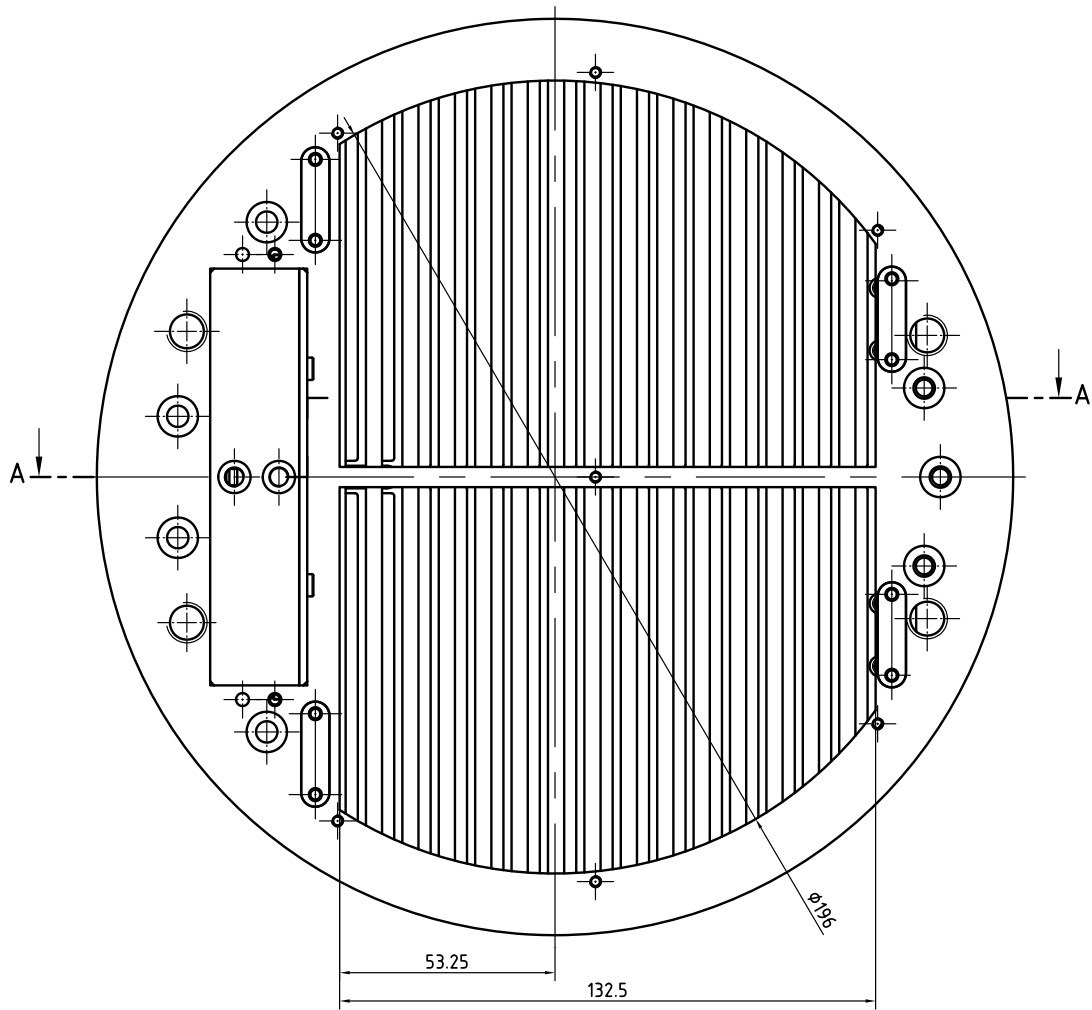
Reduzierter Ausschnitt aus der Zusammenbauzeichnung des Prototypen
